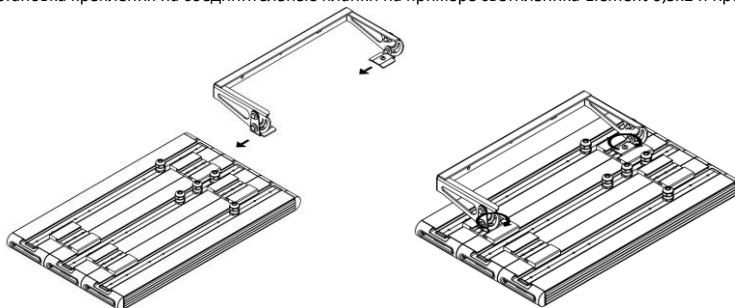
Установка крепления на соединительные планки на примере светильника Element 0,5x3 и Крепления Скоба большая с регулировкой.
